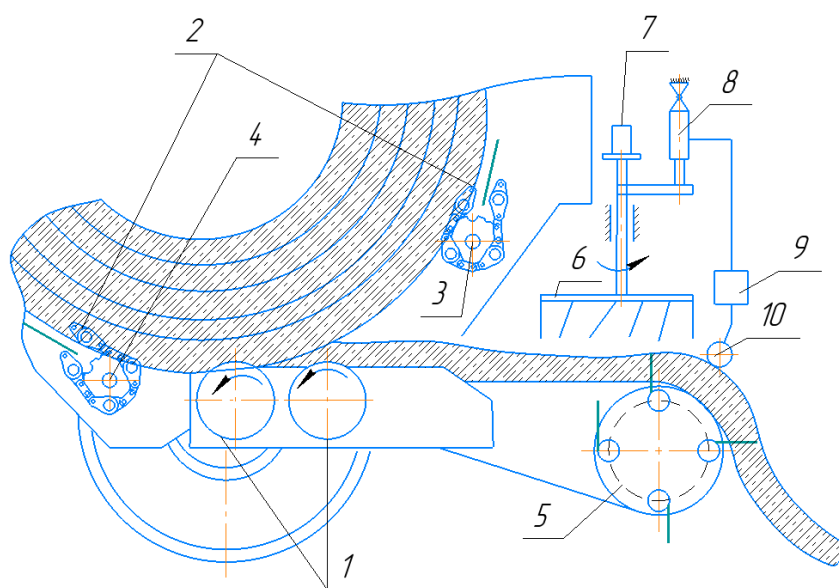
Схема пресс-подборщика с разравнивающим устройством:
